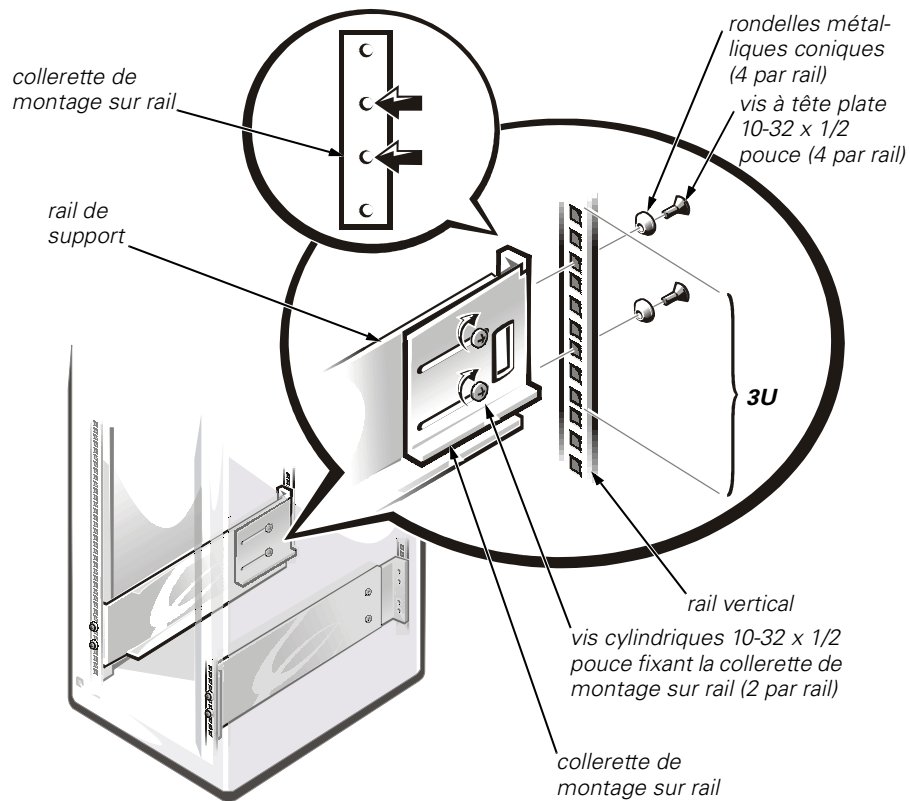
Montage de l'assemblage de rail de support au rail vertical arrière
